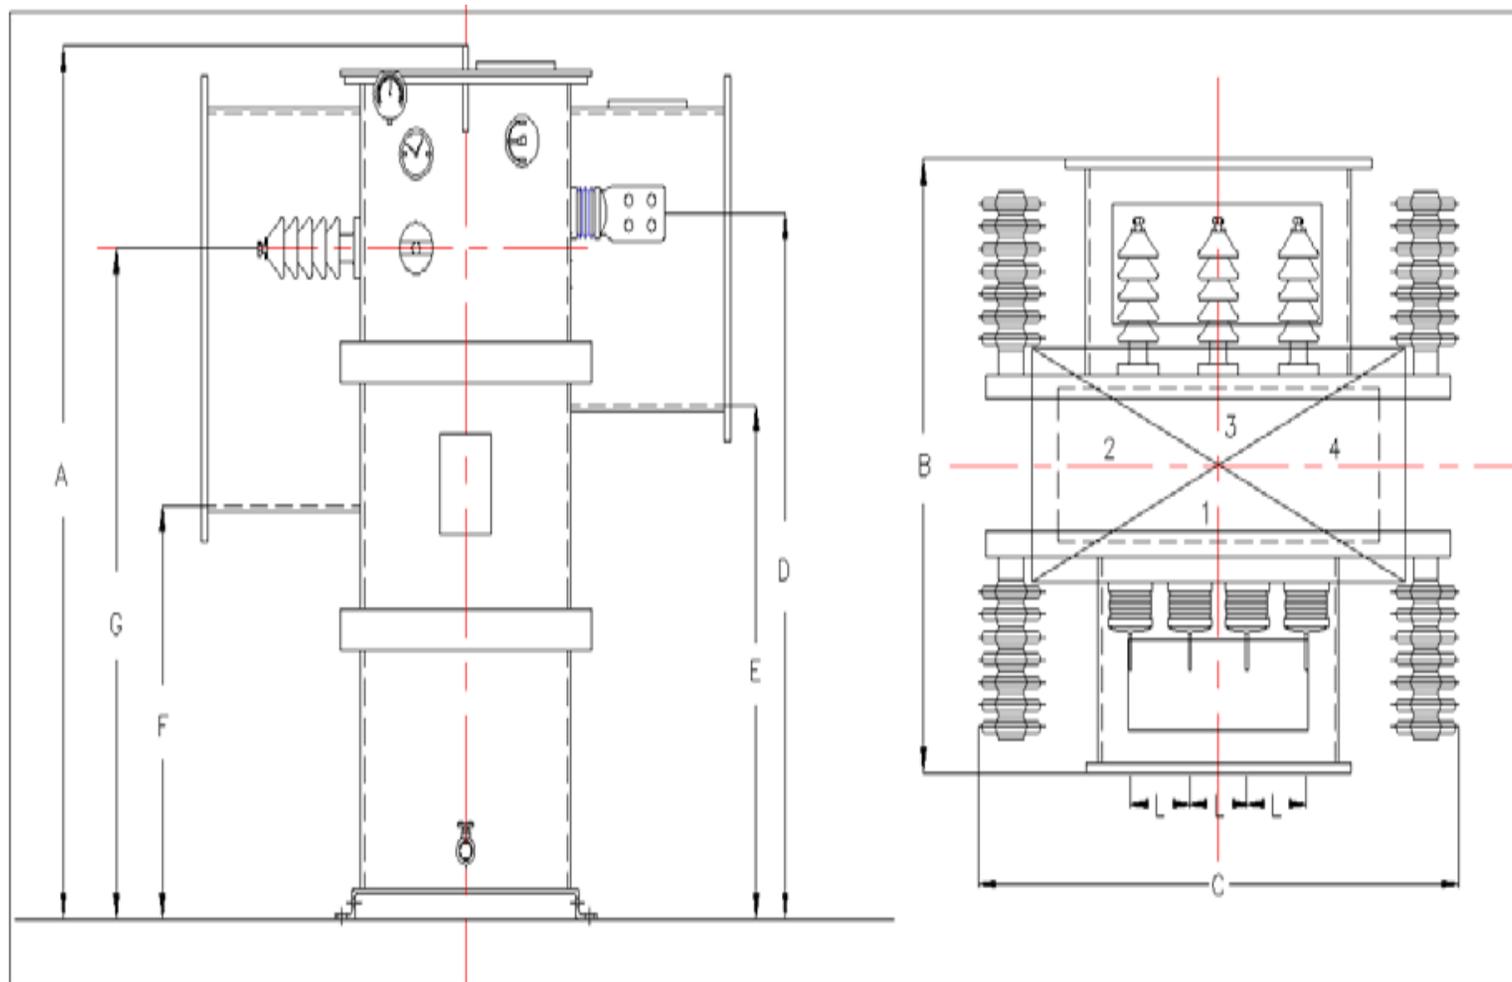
DIMENSIONES DE UN TRANSFORMADOR
